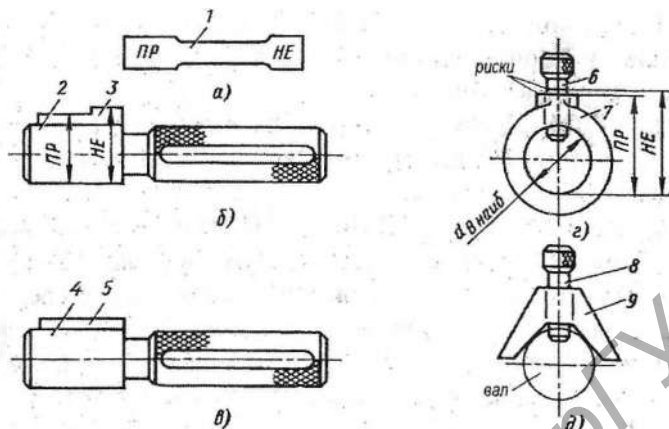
Контроль шпоночных соединений: а — плоский калибр-пробка; б — гладкий калибр-пробка со ступенчатой предельной шпонкой; в — гладкий калибр-пробка со шпонкой; г — кольцевой калибр; д — калибр-призма [10, с. 375]
